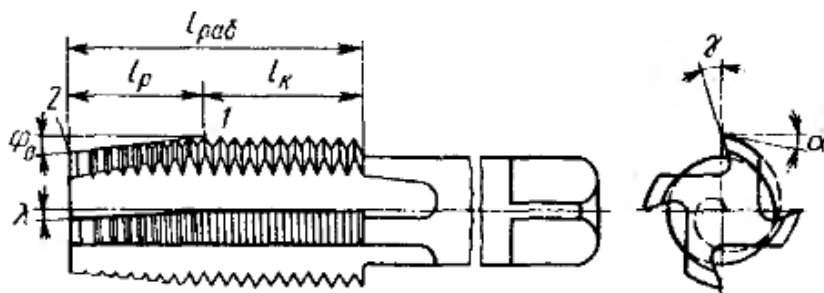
Геометрические и конструктивные параметры резьбонарезного метчика
